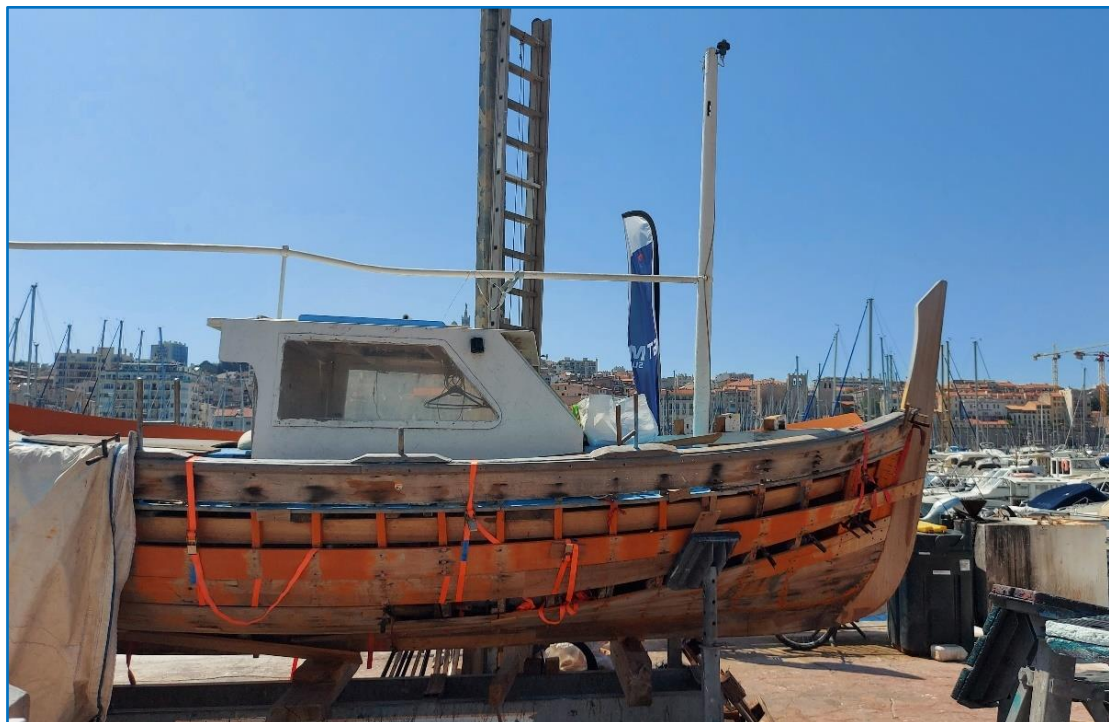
Bateau en bois en construction sur le vieux port de Marseille
